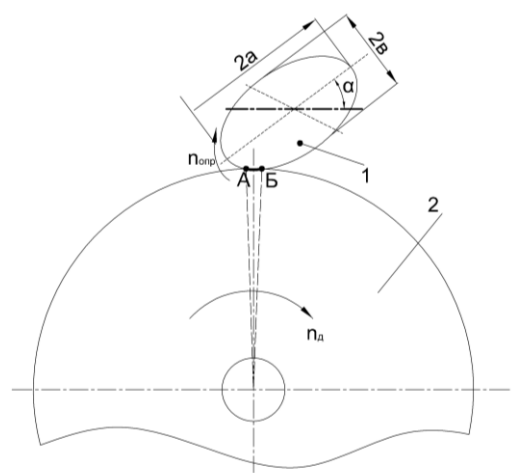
Схема контактирования точки 1, принадлежащей заготовке, совершающей эллиптическое движение, с поверхностью распиловочного диска 2
